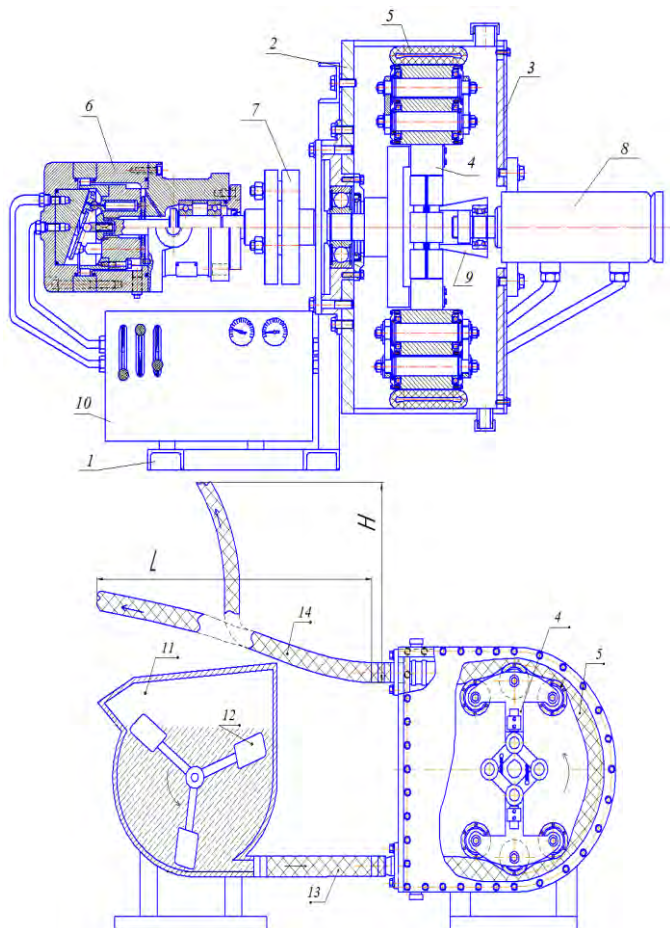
Универсальный беспоршневой (шланговый) бетононасос с гидравлическим приводом: 1 – рама; 2 – корпус насоса; 3 – крышка корпуса; 4 – ротор с роликами; 5 – гибкий шланг; 6 – гидромотор; 7 – муфта; 8 – гидроцилиндр; 9 – конический наконечник; 10 – гидрораспределительный узел; 11 – бункер с бетонной смесью; 12 – ворошитель. 13 – впускной патрубок; 14 – транспортный трубопровод
